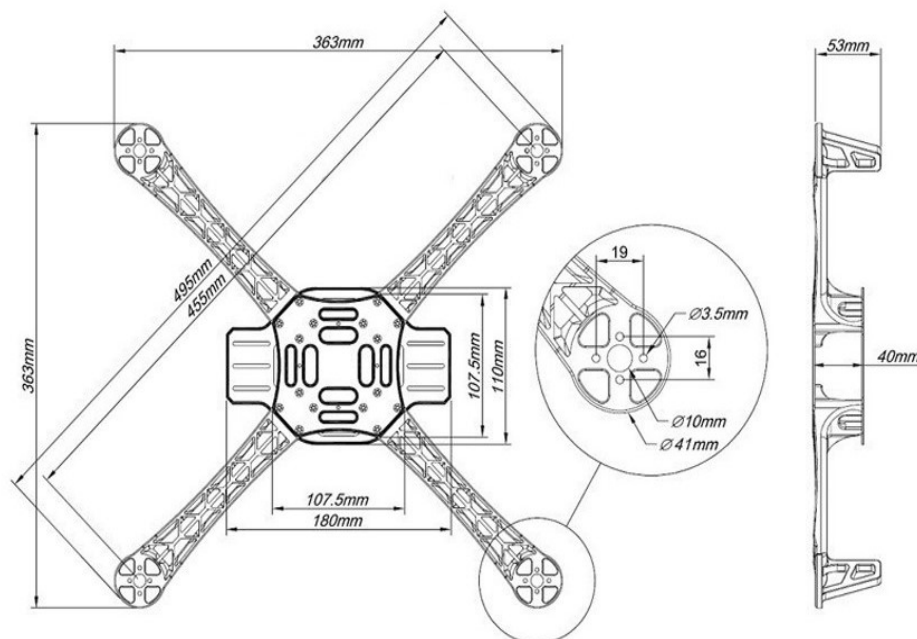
Креслення рами F450 для квадрокоптера
